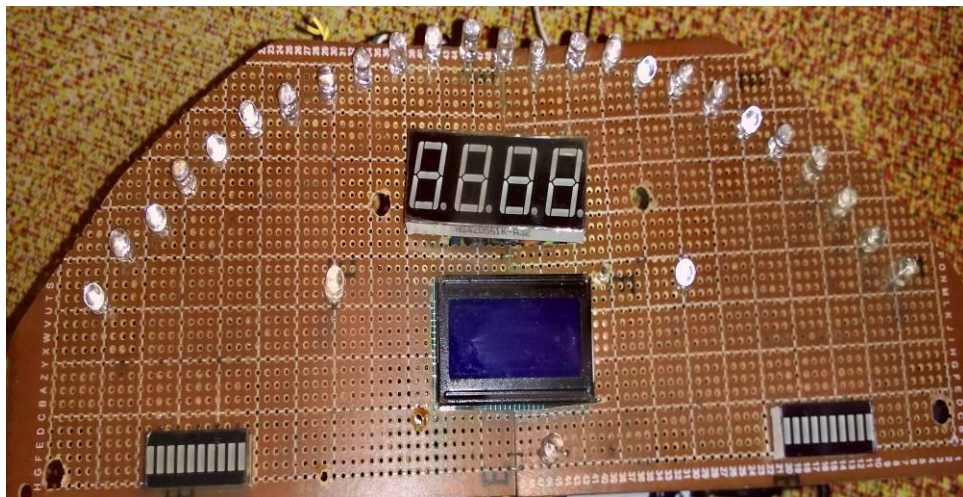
Proses Memasang dan mensolder Komponen di PCB
